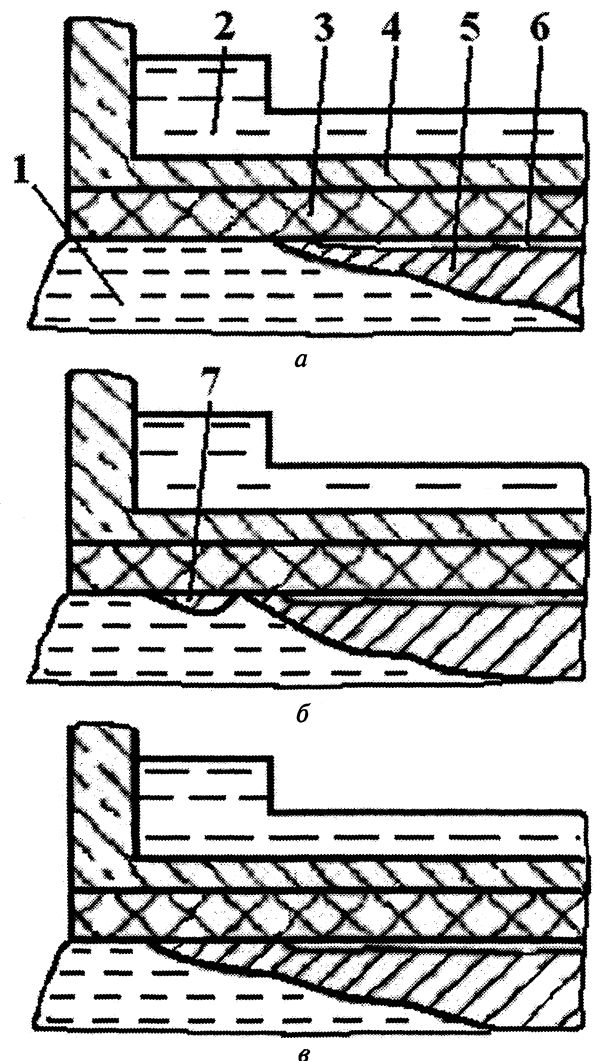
Схема формирования отливки: 1 – расплав металла; 2 – вода; 3 – рабочая втулка кристаллизатора; 4 – кристаллизатор; 5 – отливка; 6 – затор; 7 – начальная корка
